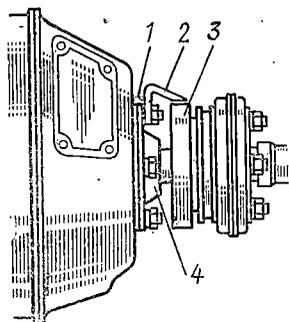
Установка стрелки для проверки угла опережения подачи топлива:
